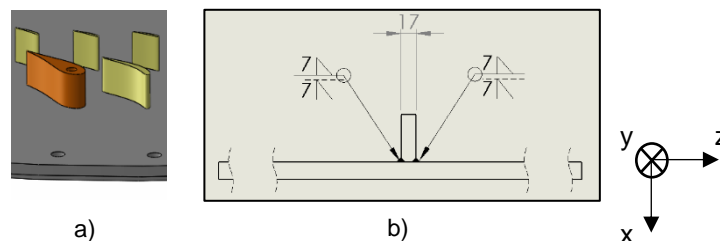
a) Componentes a ligar; b) Configuração do cordão de soldadura proposto
